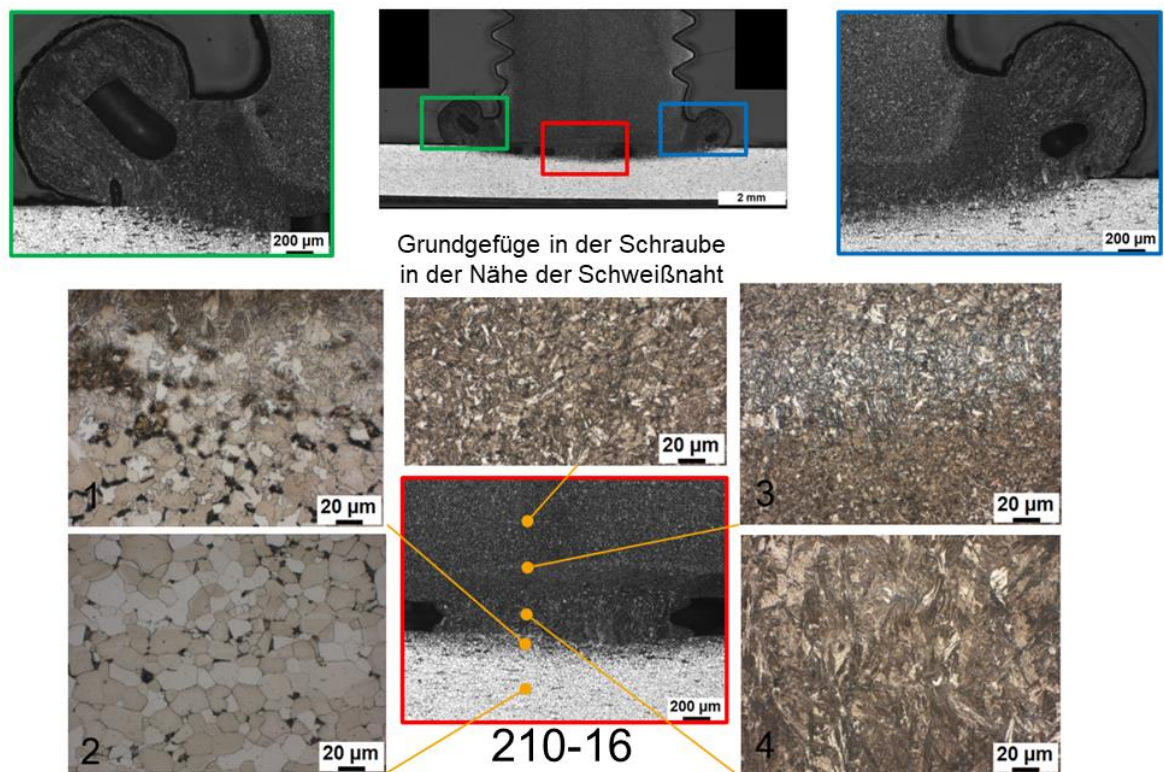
Mikrostruktur und lokale Geometrie der Schweißnaht der Bolzenprobe 210-16
